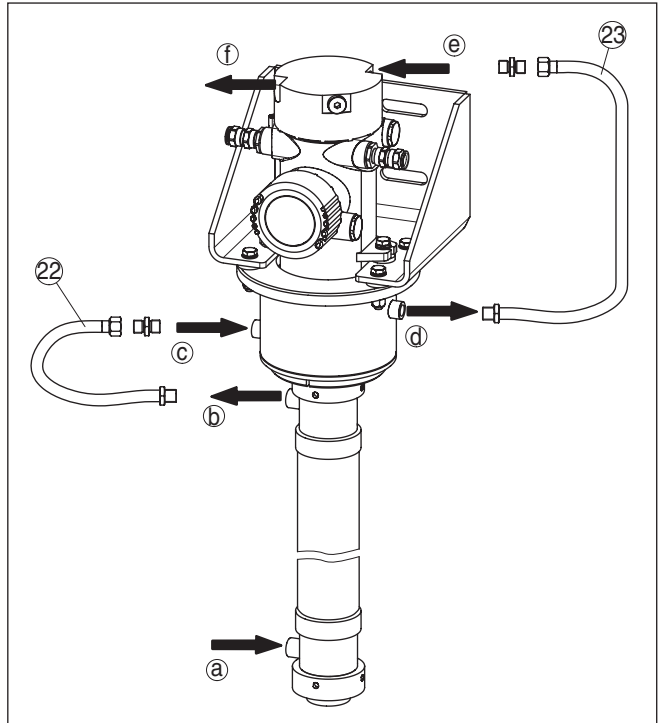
Fließrichtung des Kühlmittels (vertikale Montage, Gehäusekopf oben)
